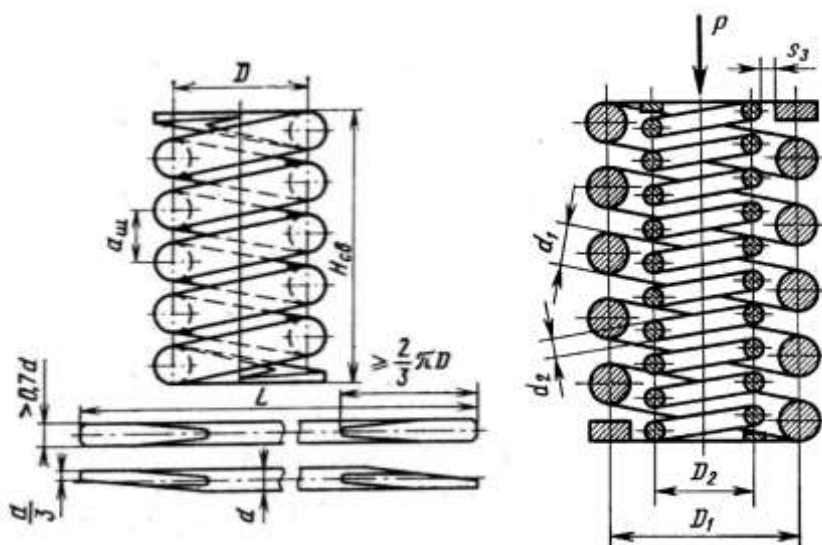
Розрахункова схема ресорного підвішування візка
